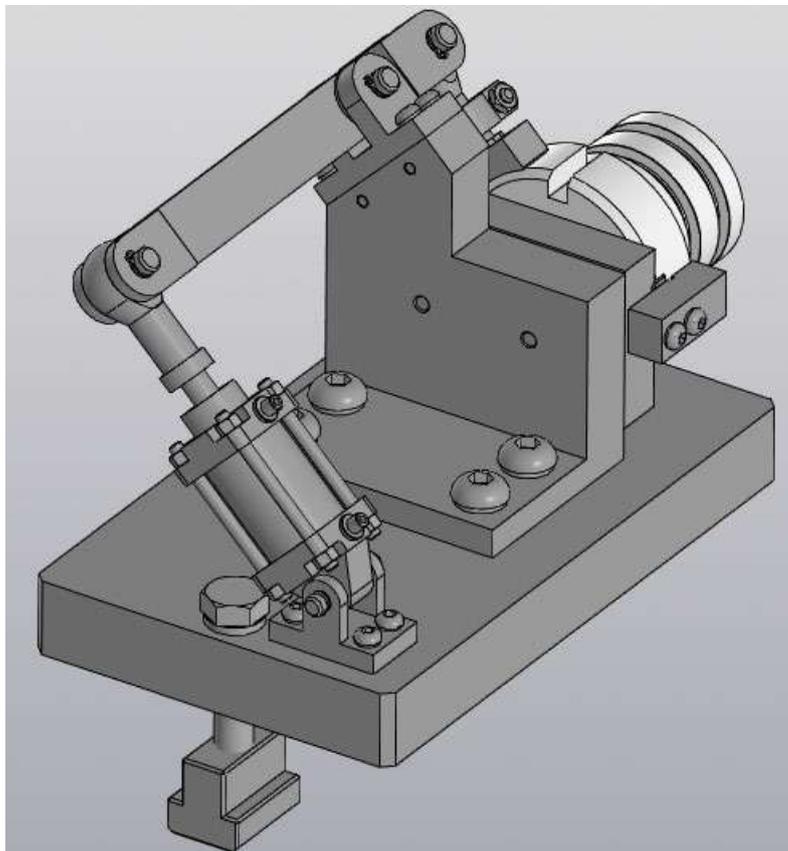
Конструкция приспособления с заготовкой, вид 2
